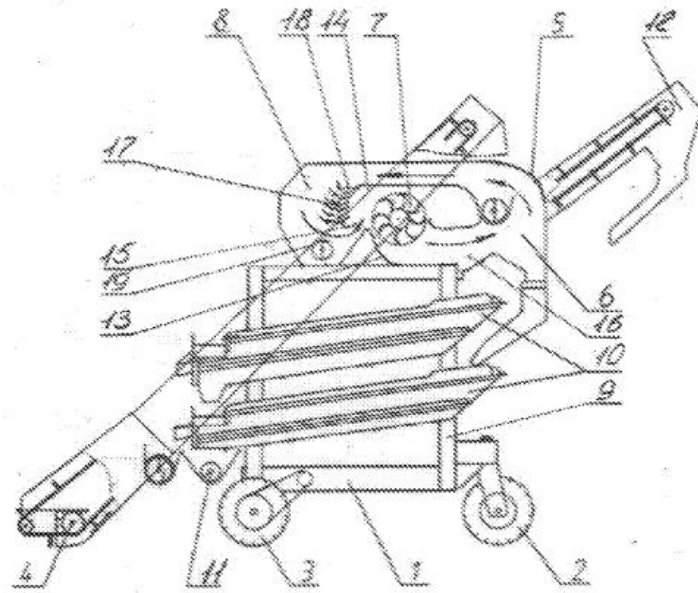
Очисник вороху самопересувний: 1 – рама; 2 – колеса; 3 – механізм самопересування; 4 – завантажувальний транспортер; 5 – пневмосепараційний блок; 6 – пневмосепараційний канал; 7 – вентилятор; 8 – осадова камера; 9 – блок решітної очистки; 10 – решітні стани; 11 – шнек; 12 – вивантажувальний транспортер; 13,14 – напрямні; 15,16 – вхідний та вихідний канал; 17 – жалюзійна поверхня; 18 – полички; 19 – шнек для легких домішок.
